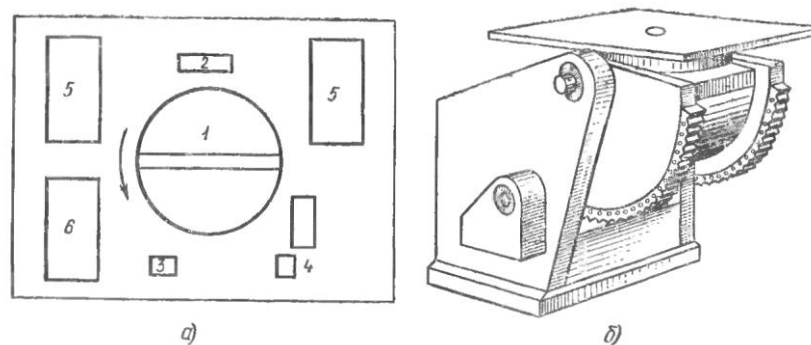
Устройства, которые улучшают условия труда сварщика: а - рабочее место в случае сварки значительного числа мелких деталей; б - манипулятор сварочный
